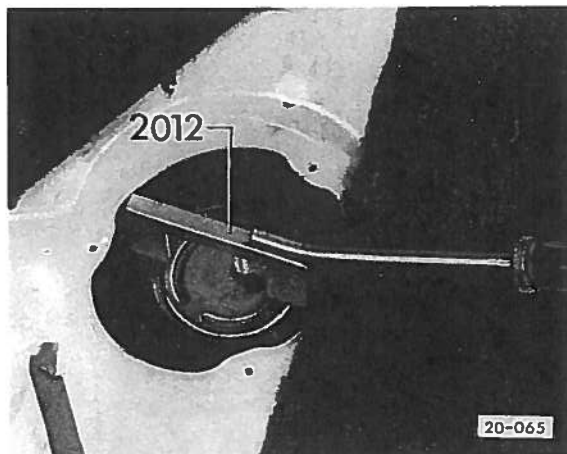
Dépose du transmetteur d'indicateur de niveau de carburant
